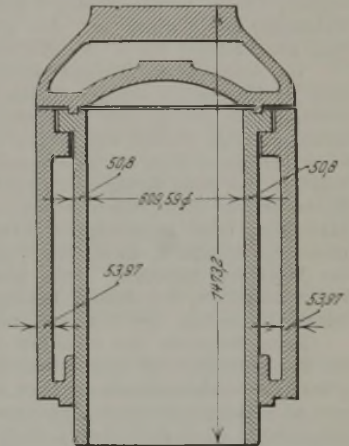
Englischer Dieselmotorzylinder. Gewicht = 6096 kg.
